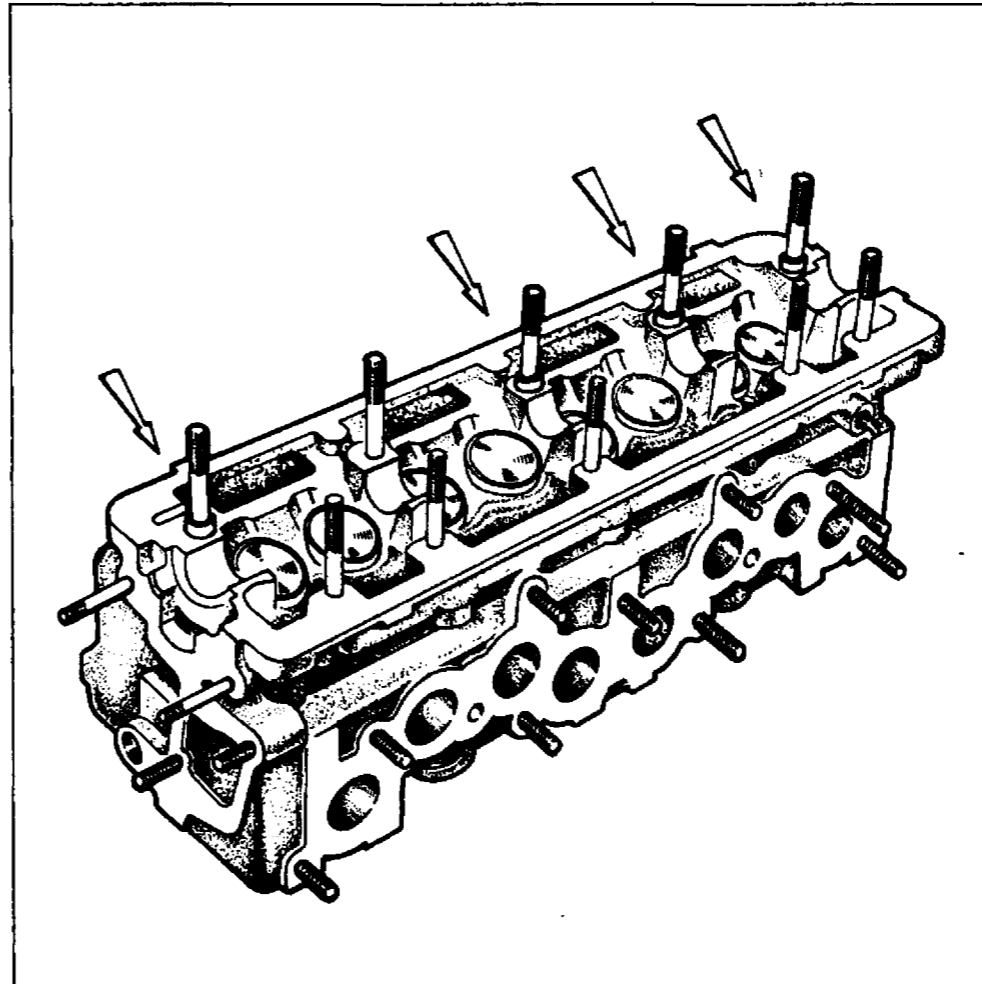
Установочные втулки корпусов подшипников распределительного вала
